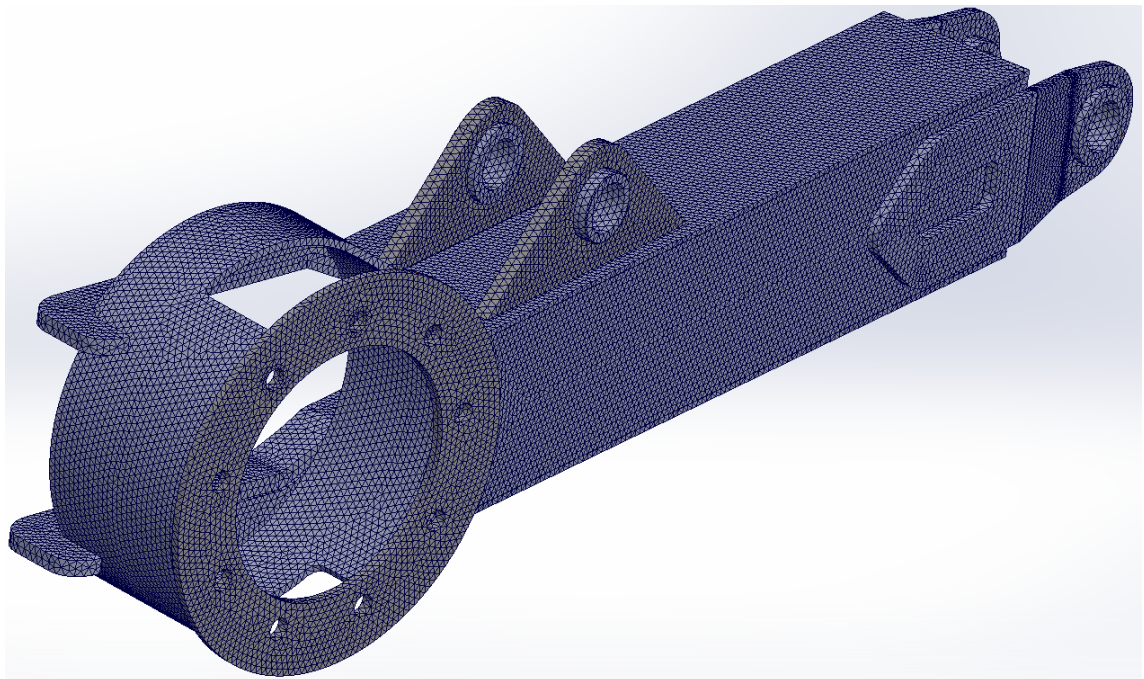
Mallado del módulo soldado de la pata motriz izquierda.
